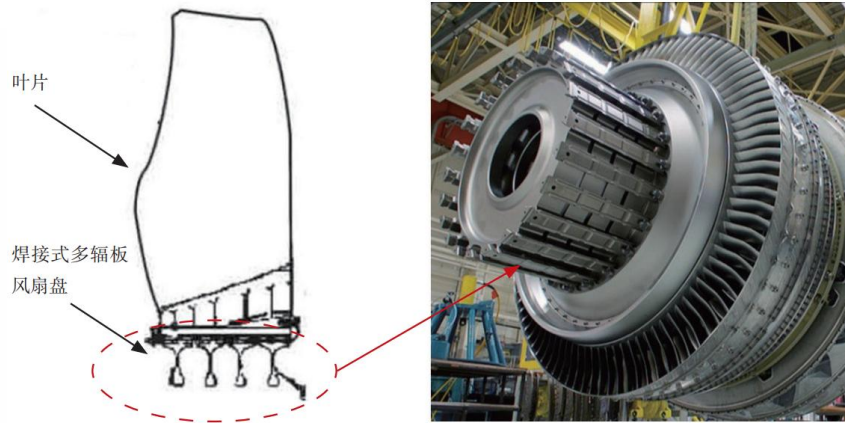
GE90-115B 发动机惯性摩擦焊风扇盘组件
